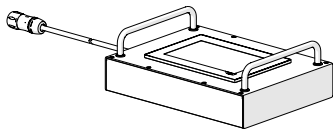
Aufbau des FAST 3000-Werkzeugs
